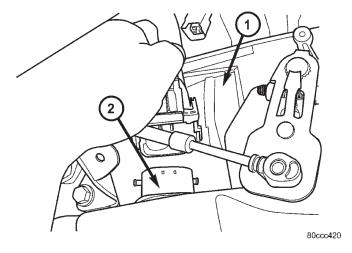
Desconexión del conjunto de solenoide de la transmisión y TRS
